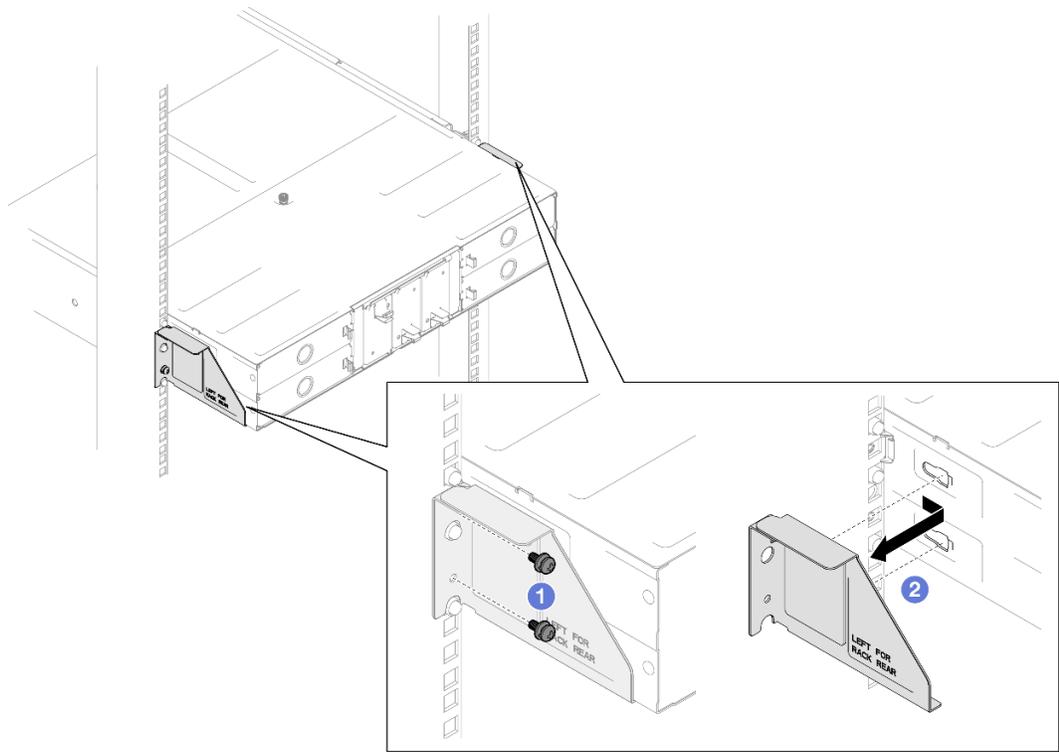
Entfernen von Transporthalterungen für 29 Zoll oder 28,31 Zoll tiefe Racks
